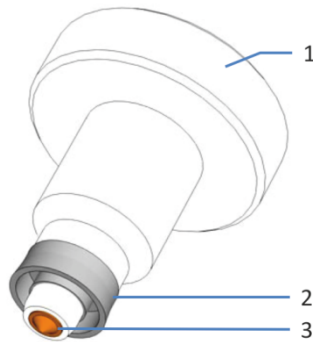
Entlüftungsschraube mit integrierten Dichtungen
